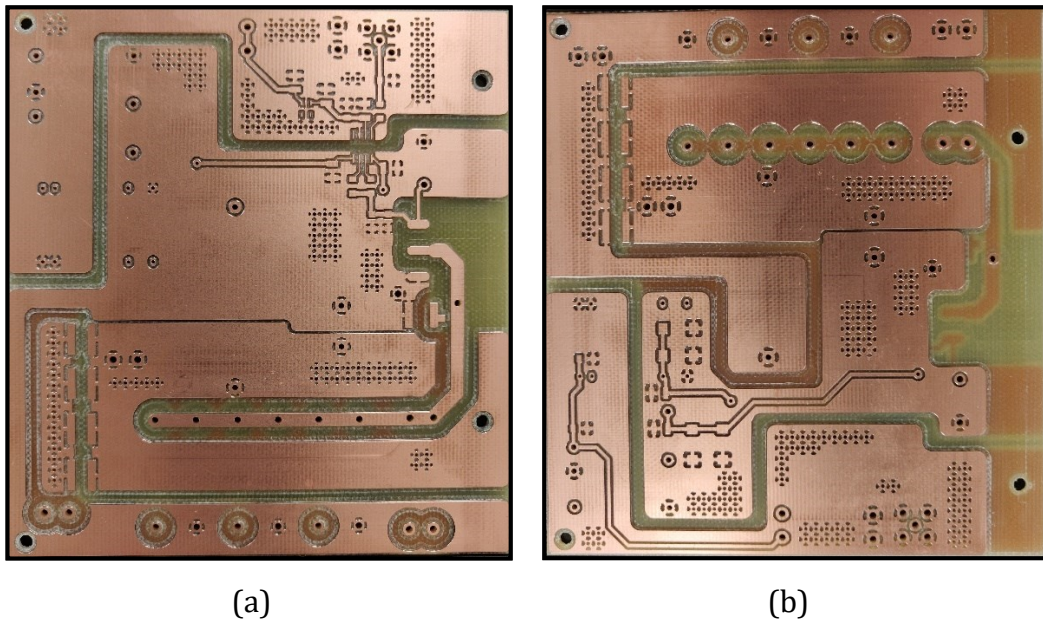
(a) Vista de la parte superior y (b) vista de la parte inferior de la PCB construida.
